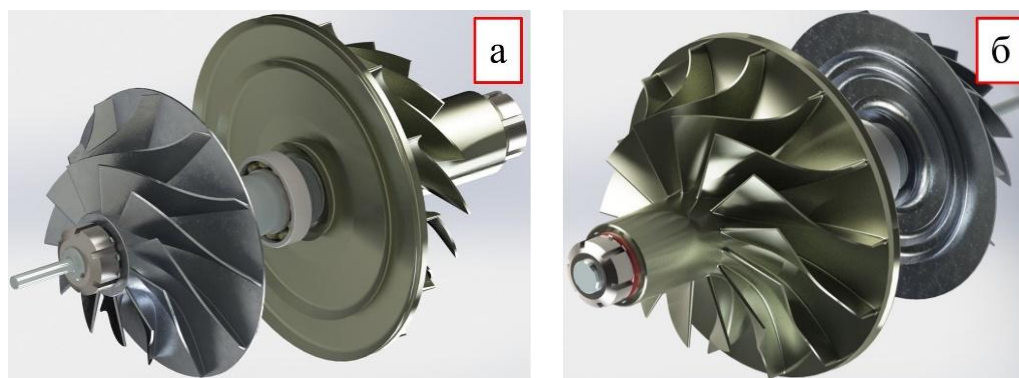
Общий вид ротора малоразмерного газотурбинного двигателя со стороны рабочего колеса компрессора (а) и рабочего колеса турбины (б)
